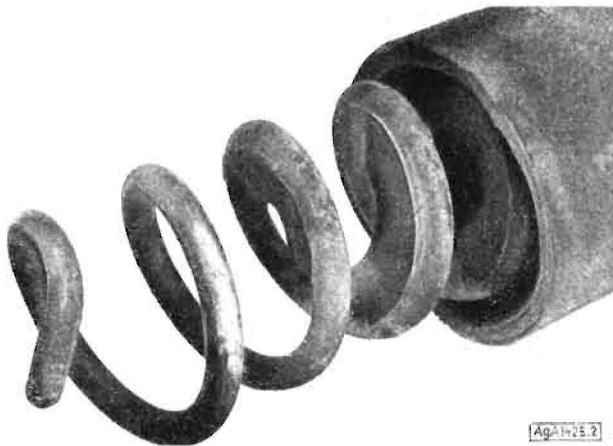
Kopfstück zum Spiralentlader. Ausführungsform Moser-Horn, Wirtschaftspatent angemeldet.
